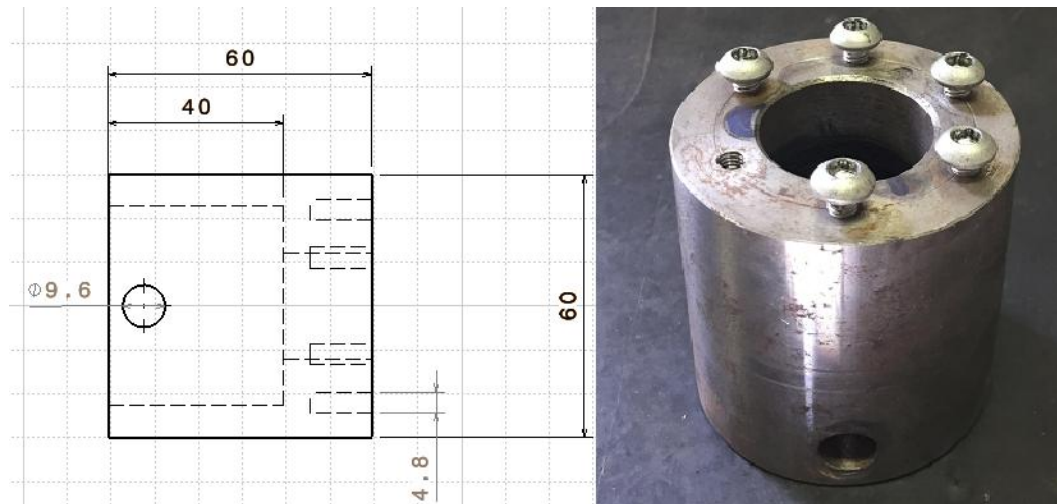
Flange de fixação do disco de freio ao eixo (Autor).
